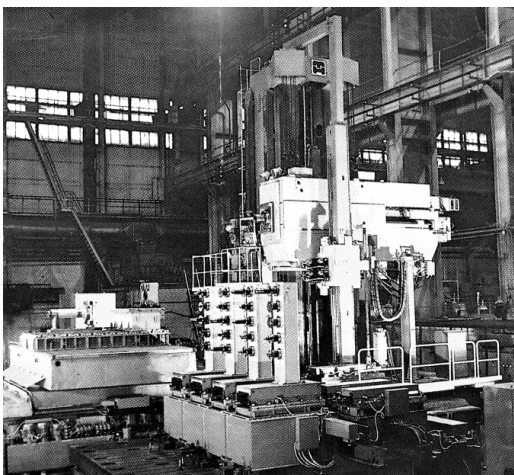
Тяжелый многоцелевой станок сверлильно-фрезерно-расточной группы с поворотным-подвижным столом для обработки корпусных деталей массой до 200 т
